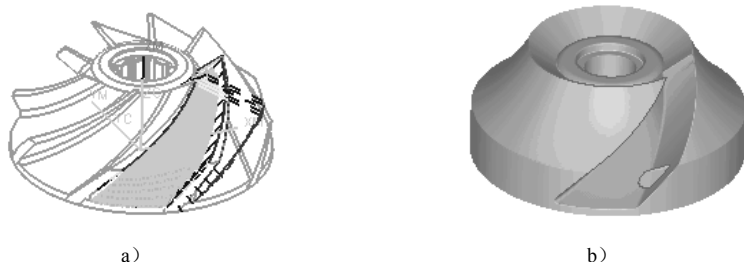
发动机叶轮曲面数控加工的“刀具路径”和“实体切削验证”
